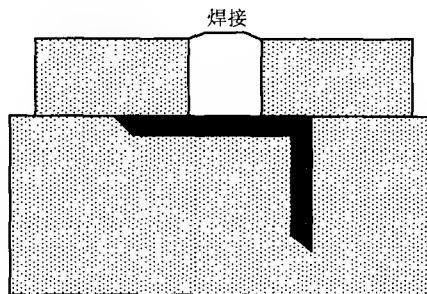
用于不锈钢包层操作的焊接接头形式
